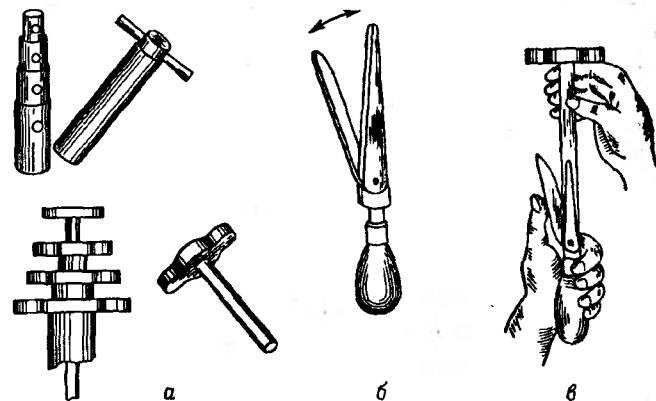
Наборы сверл (а), нож для точки сверл (б) и заточка сверл (в)
